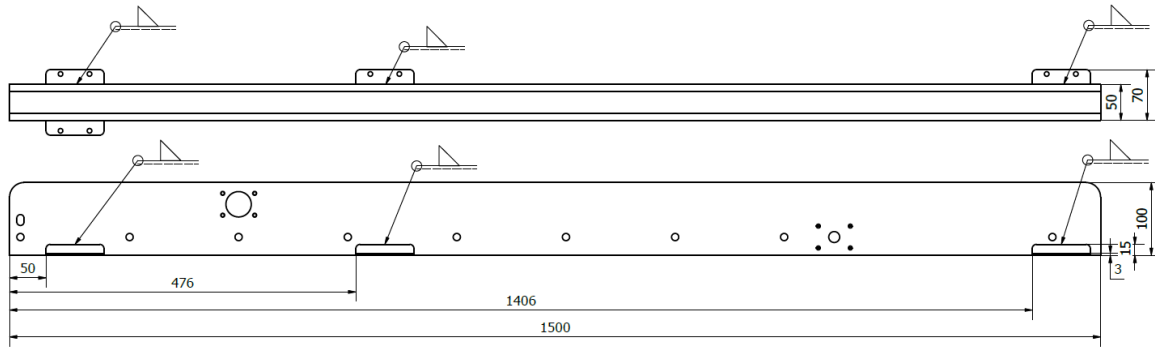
Esquema de soldadura dos suportes do caleiro do sistema de fornecimento, medidas em mm e símbolos normalizados de soldadura.
